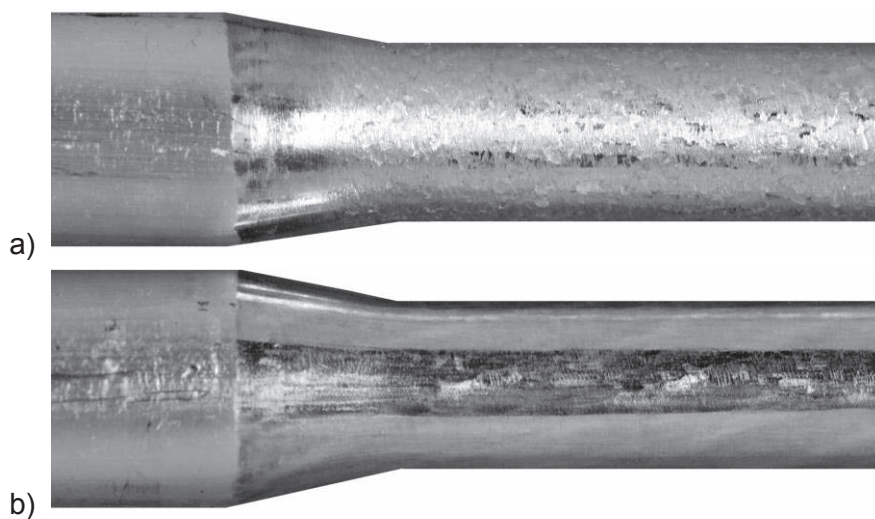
Trocken rundgeknetete Aluminiumrohre ($v_f = 500 \text{ mm/min}$); a) mit konventionellen Werkzeugen, b) mit beschichteten Werkzeugen.
